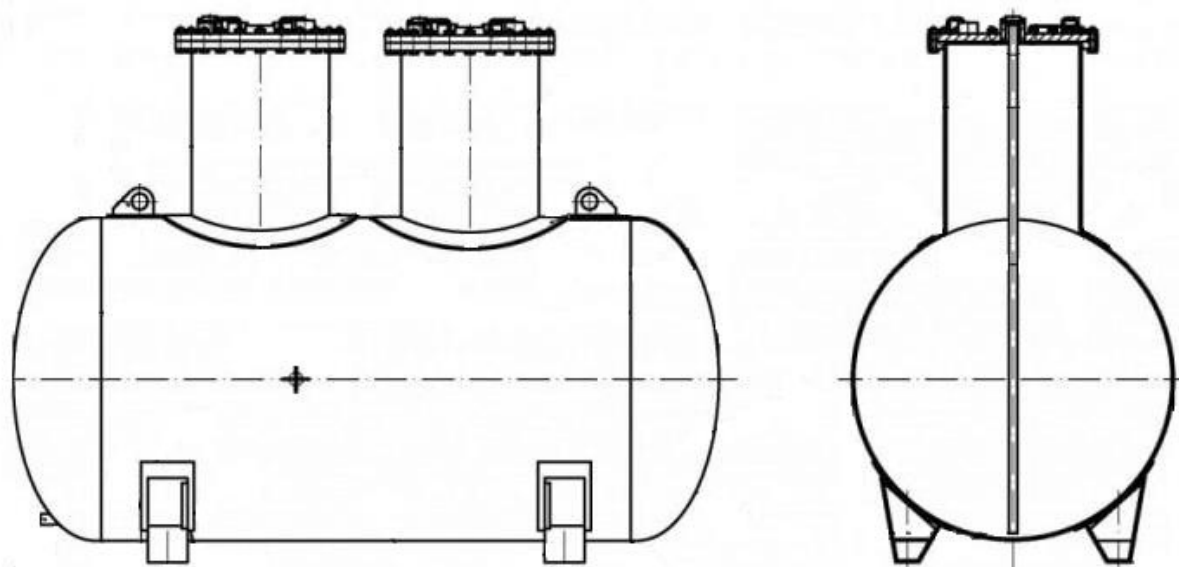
Эскиз общего вида резервуаров РГС-50
